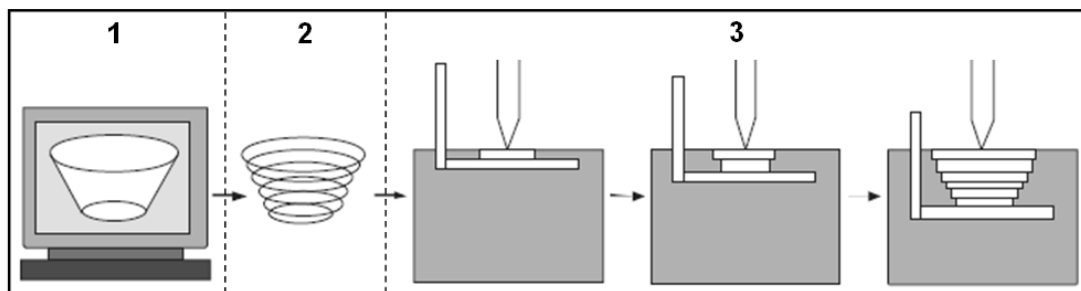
Principe de la fabrication additive. 1 : dessin de la pièce en 3 dimensions, 2 : tranchage de la pièce en sections parallèles, 3 : fabrication de la pièce couche par couche
